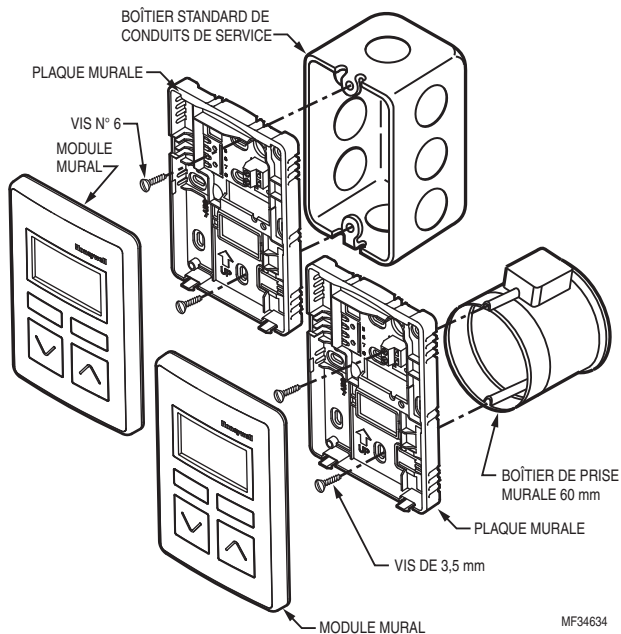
Montage sur boîtier standard de conduits de service ou boîtier de prise murale de 60 mm
